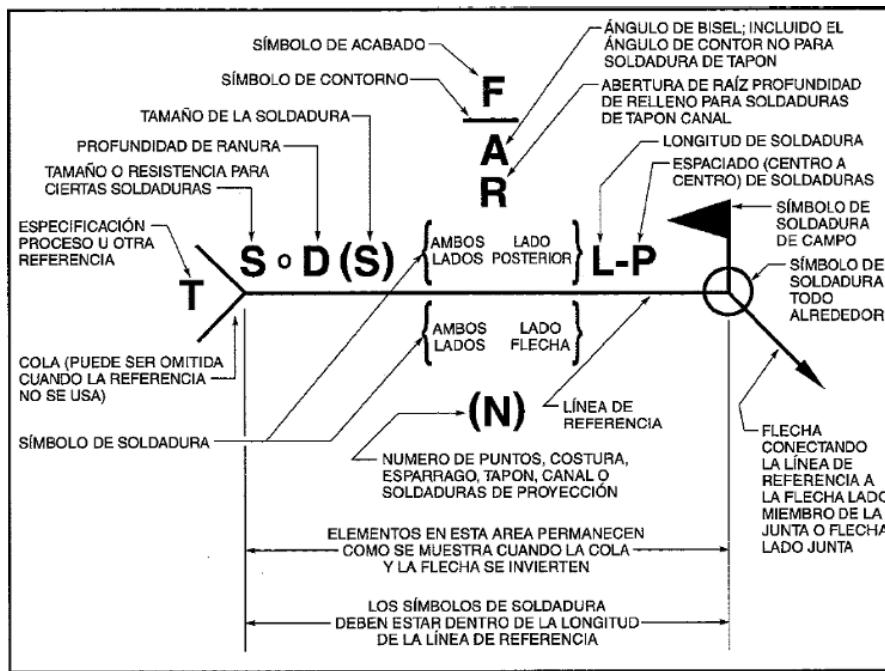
Simbología de Soldadura. Fuente: Apuntes de Catedra de Unión de Materiales por soldadura.
